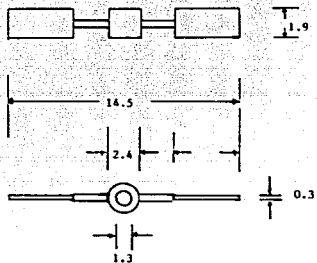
DIMENSIONES DEL IMPULSOR DE PALETA.
